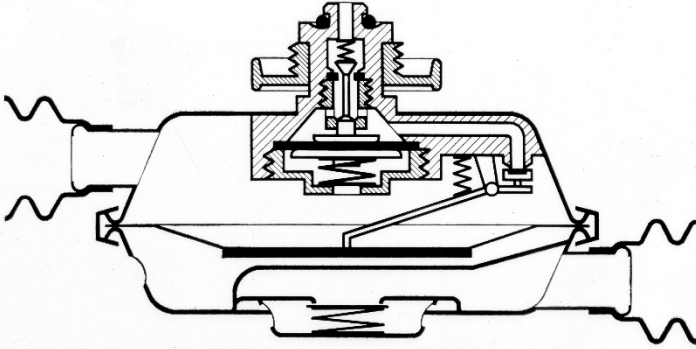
Schnittzeichnung des Lungenautomaten PA61/II
